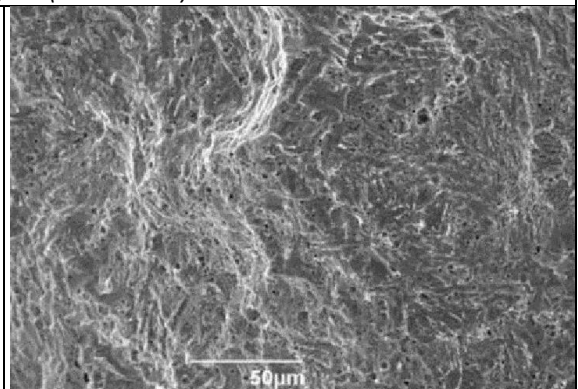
Superficie de fractura inclinada con presencia de dimples, característica de una fractura dúctil. (Fuente TGP)
